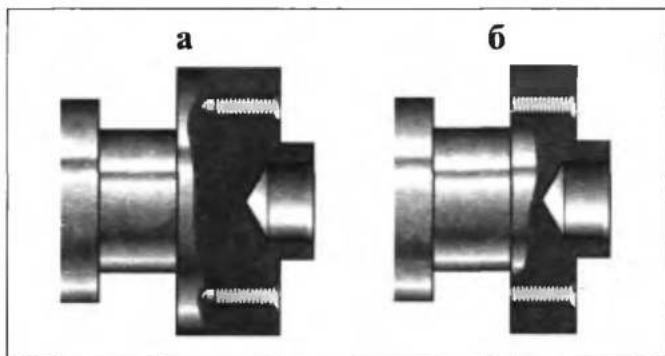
Два типа отверстий болтов крепления маховика: а — глухие отверстия (требуют увеличения ширины фланца); б — сквозные отверстия (требуют герметизации резьбы болтов)
